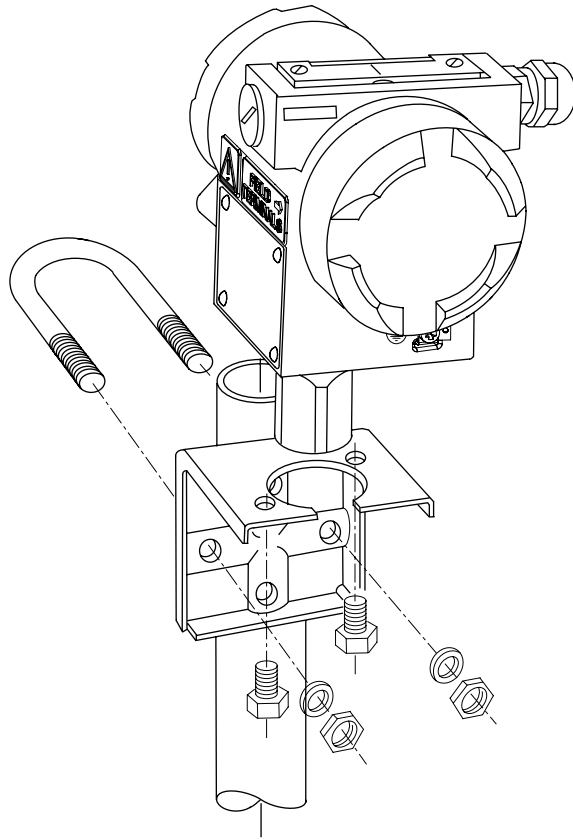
Befestigung des Messumformers mit Montagewinkel
